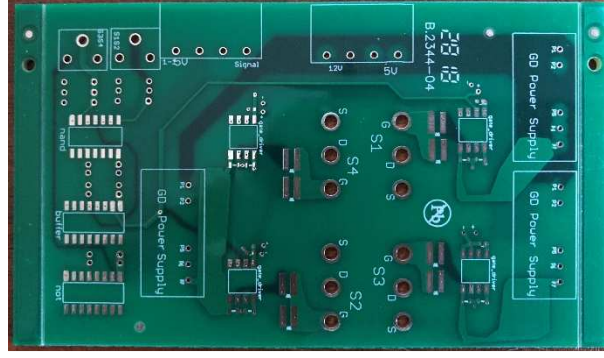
LLC rezonanslı dönüştürücü PCB tasarımı (93 mm x 113.5 mm).
